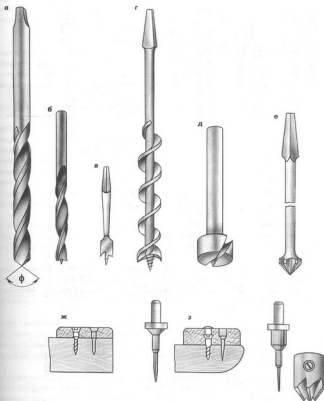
Сверла (а — д, ж, з) и зенковка (е).
